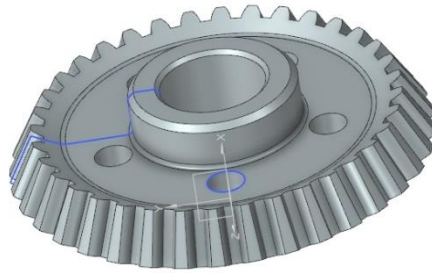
Тривимірна модель зубчастого колеса
